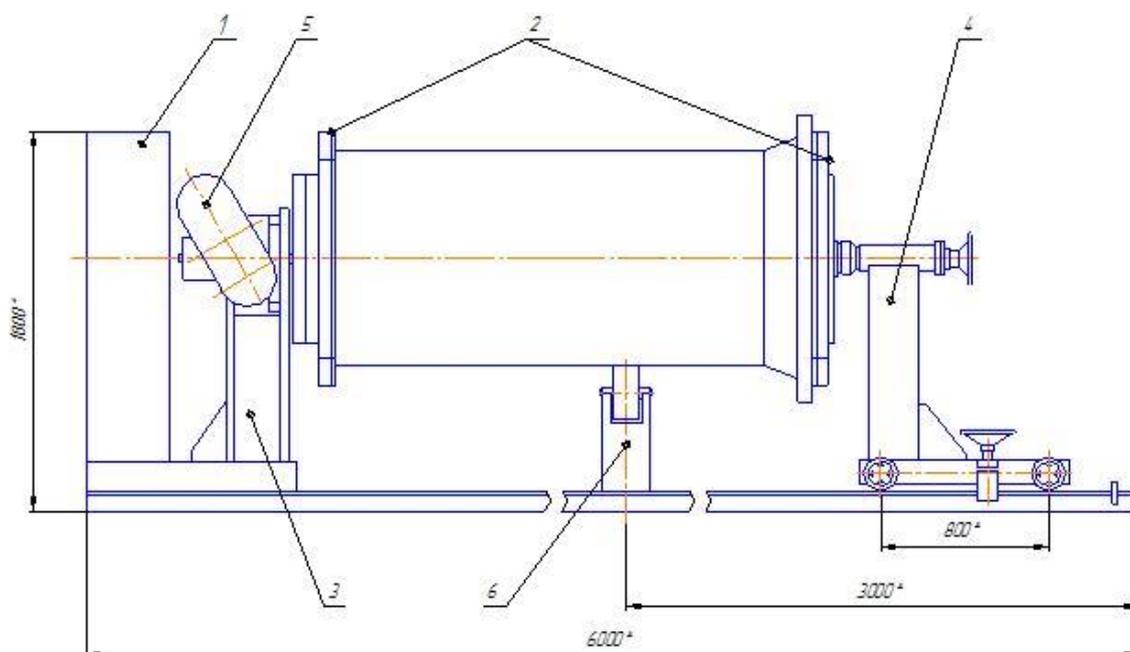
Вращатель двухстоечный М31050А (с закреплённой в нём деталью)
